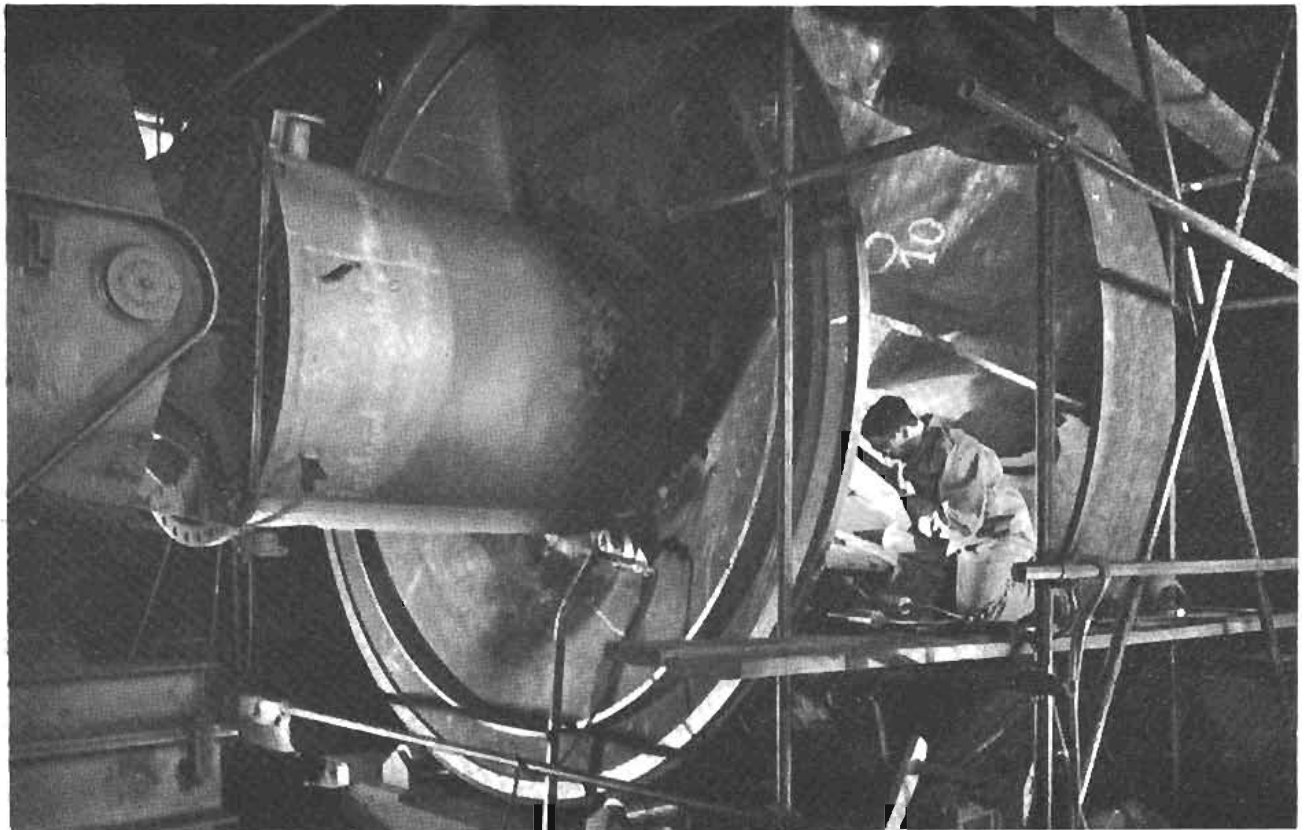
Rodete de eje horizontal en proceso de ensamble, usando soldadura de alta resistencia
